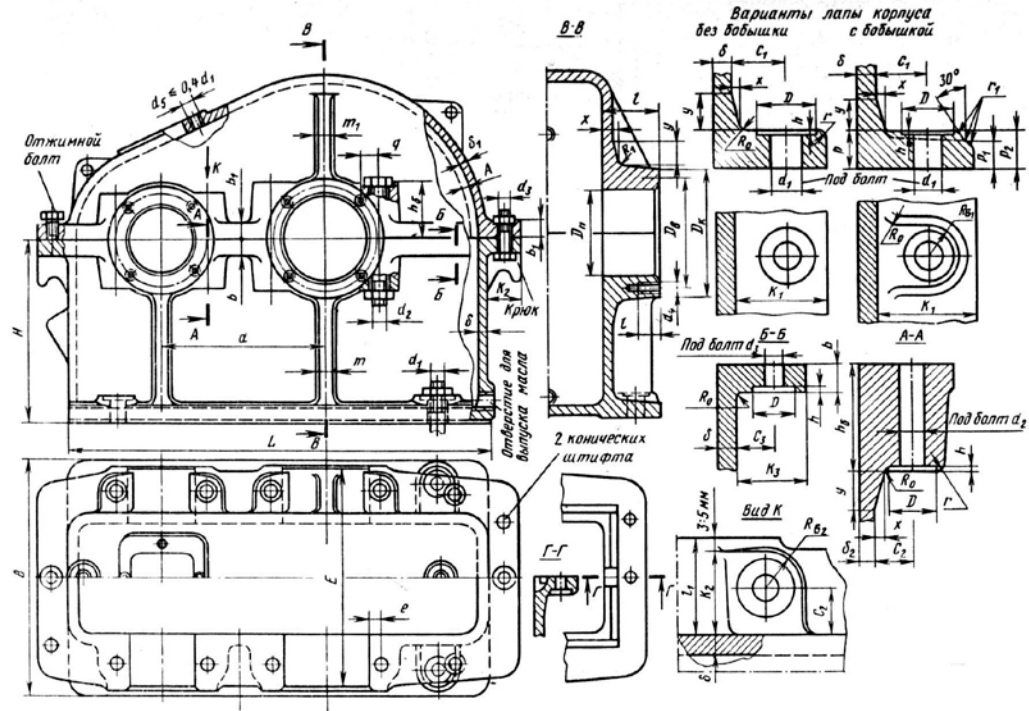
Конструктивные элементы корпуса и крышки редуктора
